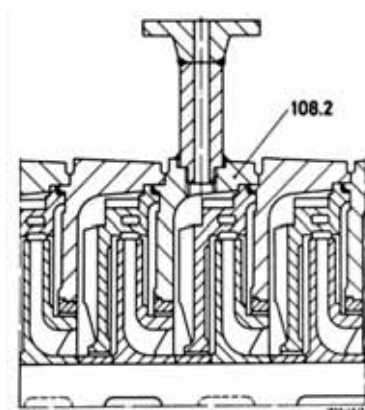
Corpo de estágio com extração intermediária roscada e soldada
